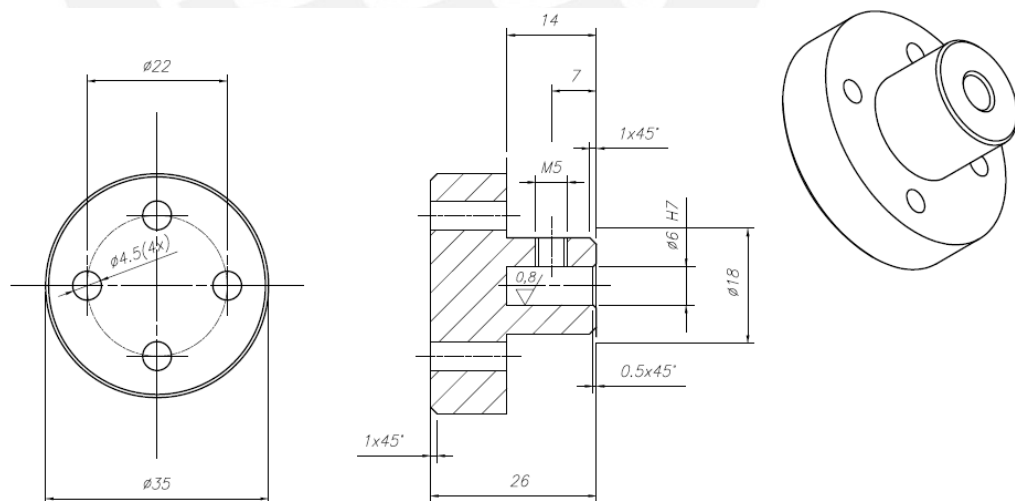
Acople para motor del prensor, L16-A3.
